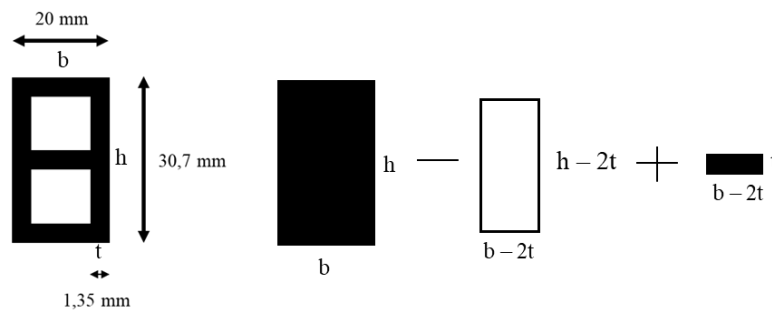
Dimensões sectionadas da seção transversal. (Autoria própria, 2025)
